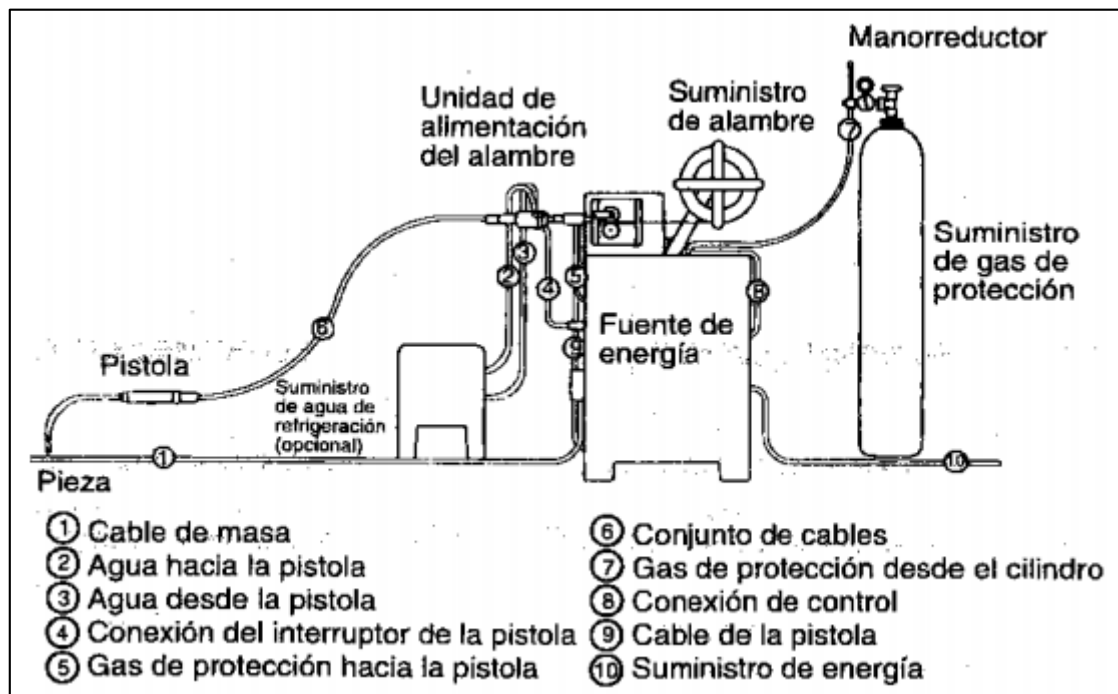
Equipo de soldeo y principales componentes del proceso GMAW
